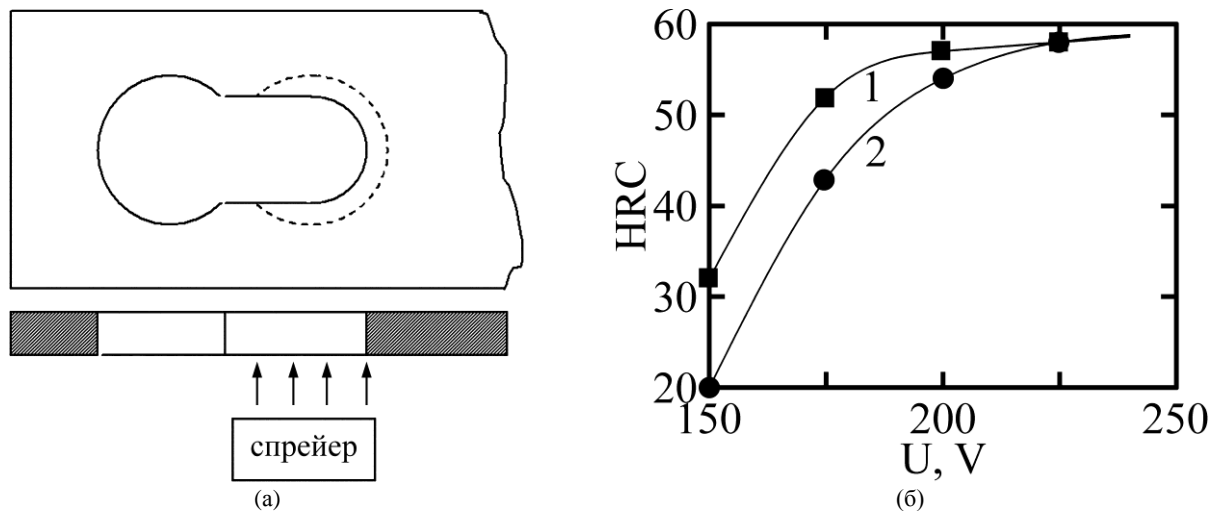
Схема струйной закалки рабочего участка планки (а) и твердость нижней (1) и верхней (2) поверхностей планки при различных напряжениях (б) [109].
